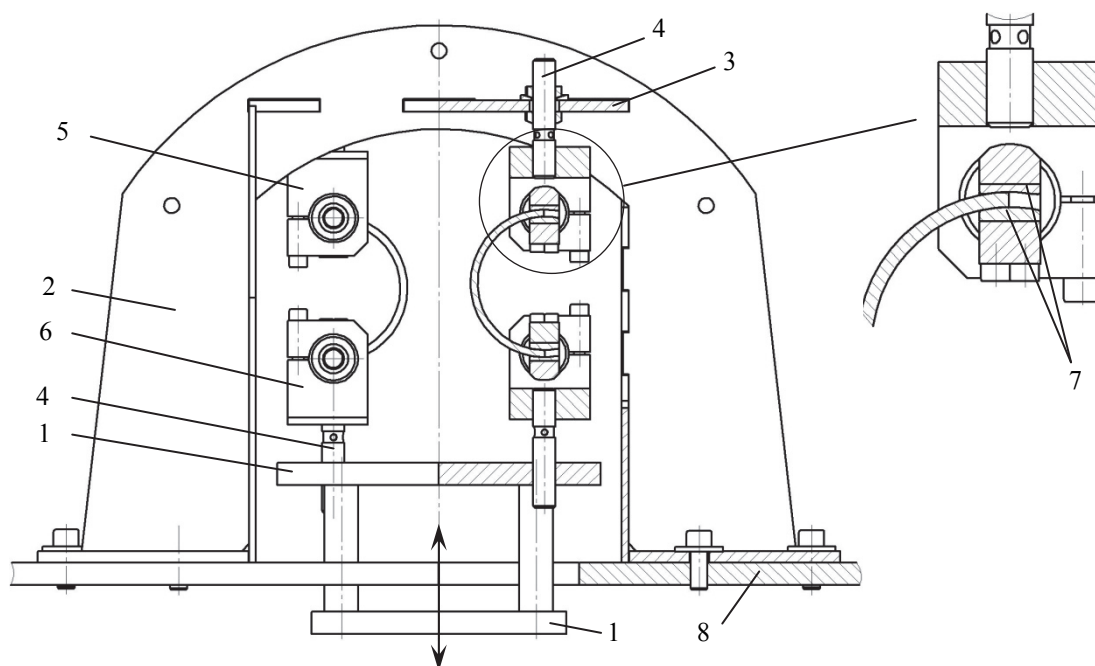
Схема приспособления для нагружения вкладышей: 1 – подвижная опора; 2 – неподвижная опора; 3 – потолочная пластина; 4 – регулировочные шпильки; 5 – верхний поворотный зажим; 6 – нижний поворотный зажим; 7 – вкладыши с цилиндрической поверхностью; 8 – станина вибростенда
